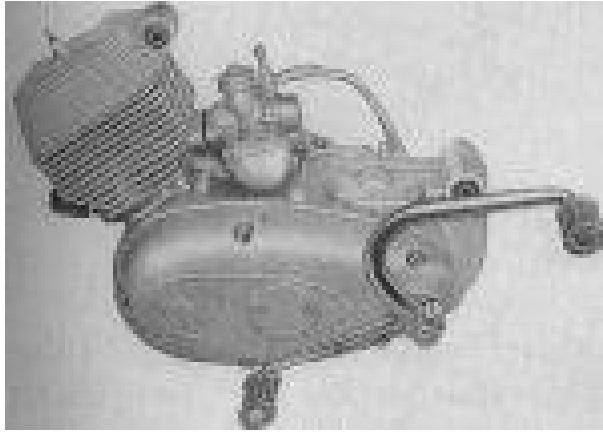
Gesamtansicht des Motors (Fahrtwind gekühlt und mit Zündspule).
